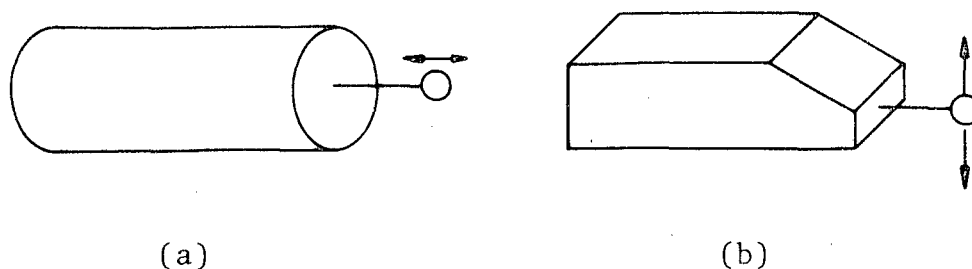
(a) Apalpador com direção de medição axial; (b) Apalpador com direção de medição transversal.
